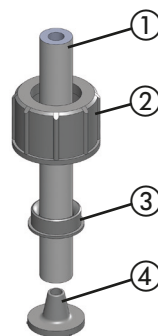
Schlauchklemmanschluss 6/12 (Innen- und Außendurchmesser in mm)
